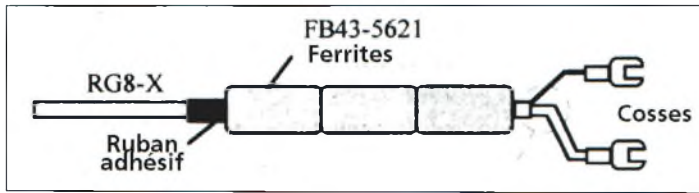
Fabrication du balun (ou du harnais de couplage).
